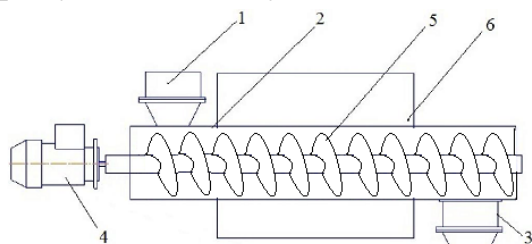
Схема и конструкция предложенного шнекового подающего устройства для установки СВЧ обработки сыпучих материалов: 1 – загрузочное устройство; 2 – камера; 3 – разгрузочное устройство; 4 – электропривод шнека; 5 – шнек из радиопрозрачного материала; 6 – рабочая камера СВЧ нагрева
